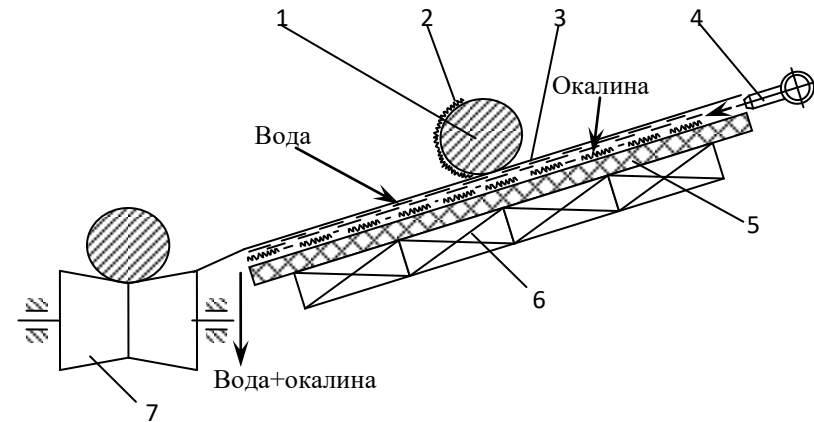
Пристрій для видалення окалини з нагрітих циліндричних заготовок (а. с. №735354): 1 – заготовка; 2 – окалина; 3 – напрямні; 4 – блок форсунок; 5 – похилий стіл; 6 – блок електромагнітів; 7 – відповідний рольганг
